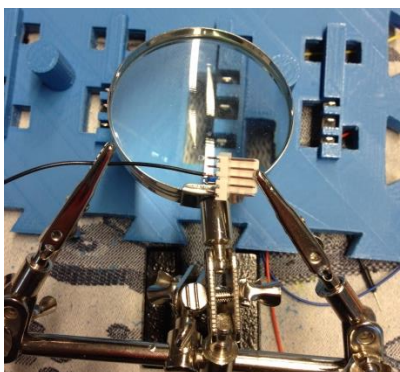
Soldagem de componentes, fonte Paulo Páscoa, 8 de junho de 2016
